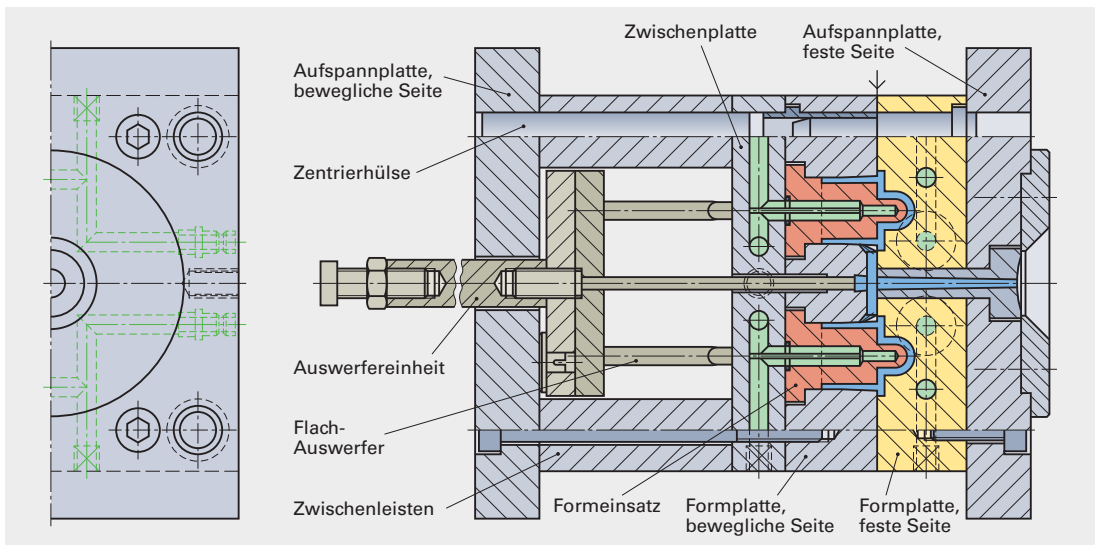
Zweiplattenspritzgießwerkzeug für Lagerzapfen
